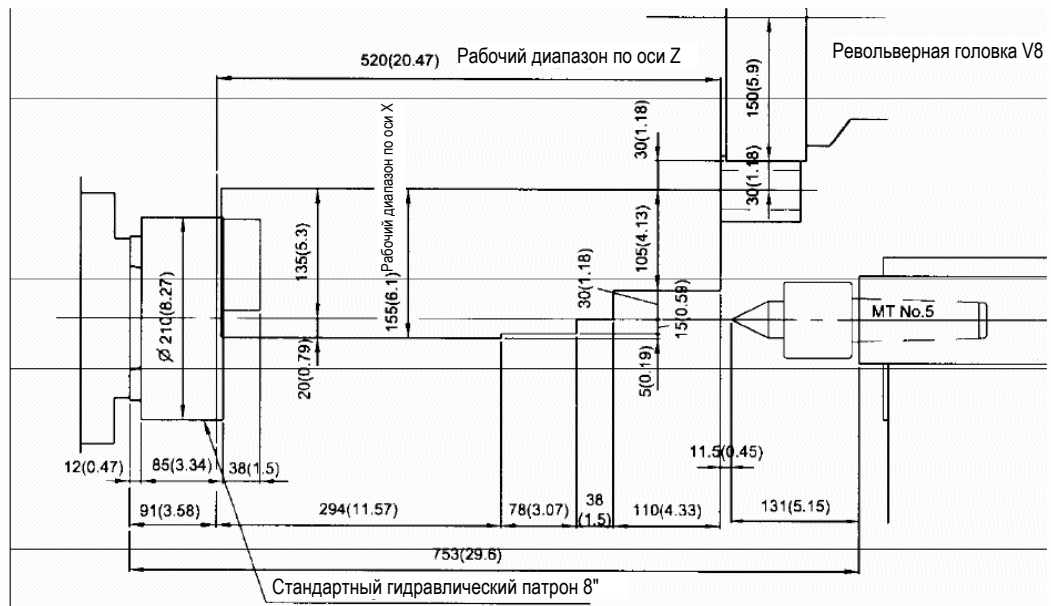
Схема рабочего диапазона (Резцедержатель внутреннего диаметра)
